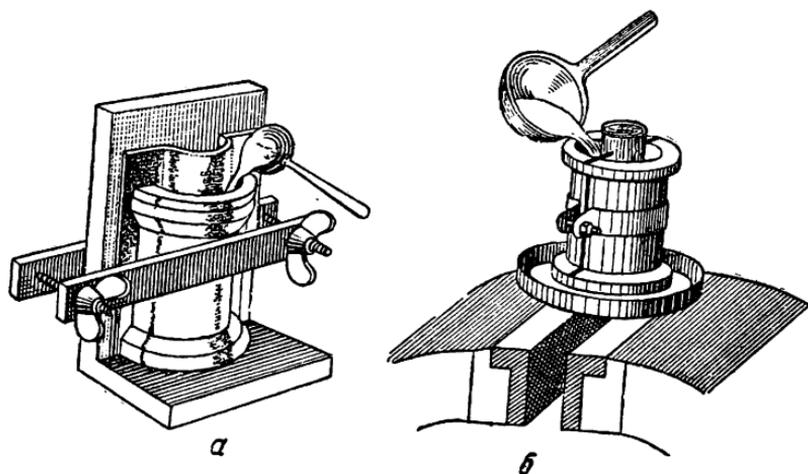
Схемы ручной заливки подшипников: а—заливка вкладыша подшипника; б—заливка втулки или вкладыша подшипника.
